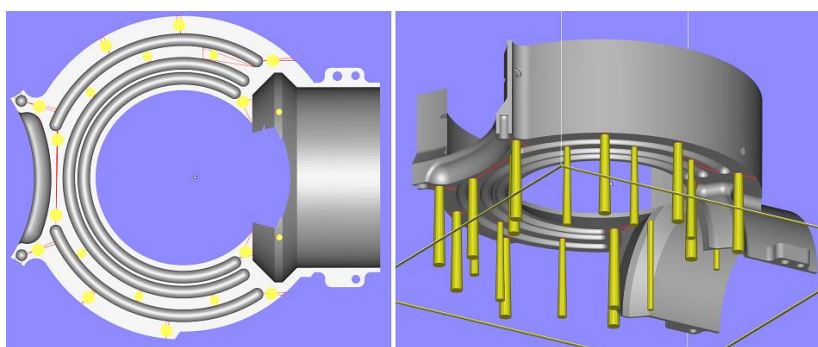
Ukázka úpravy navržených podpěrných struktur a jejich destrukce
